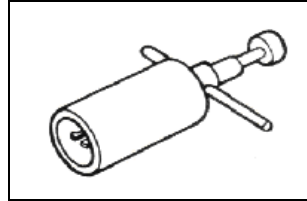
Extractor de cojinete y conjunto de válvula.
